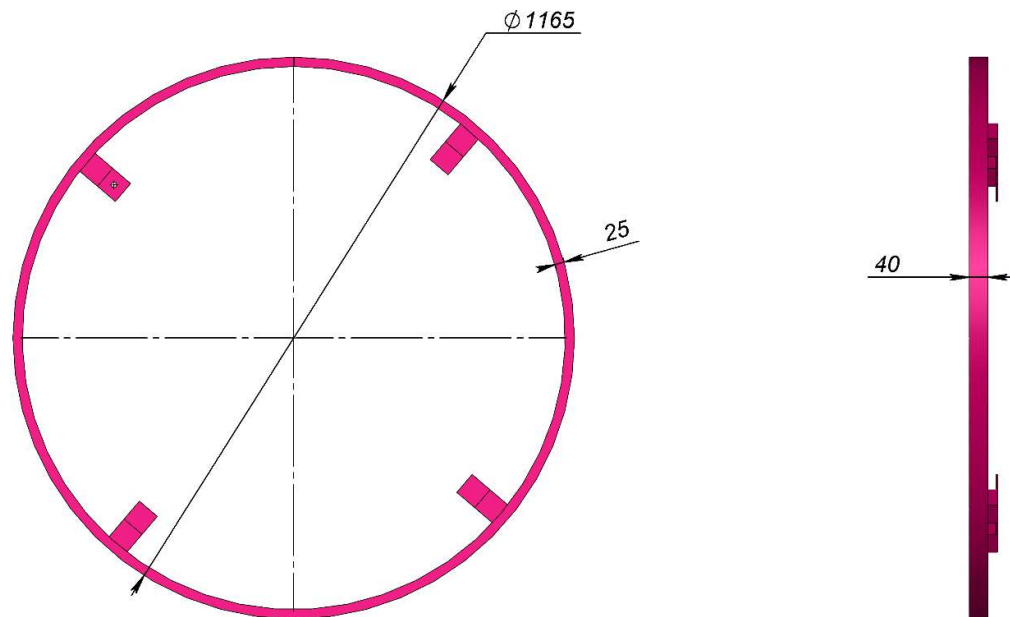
Кільцева рейка для обертання трекера за азимутом
